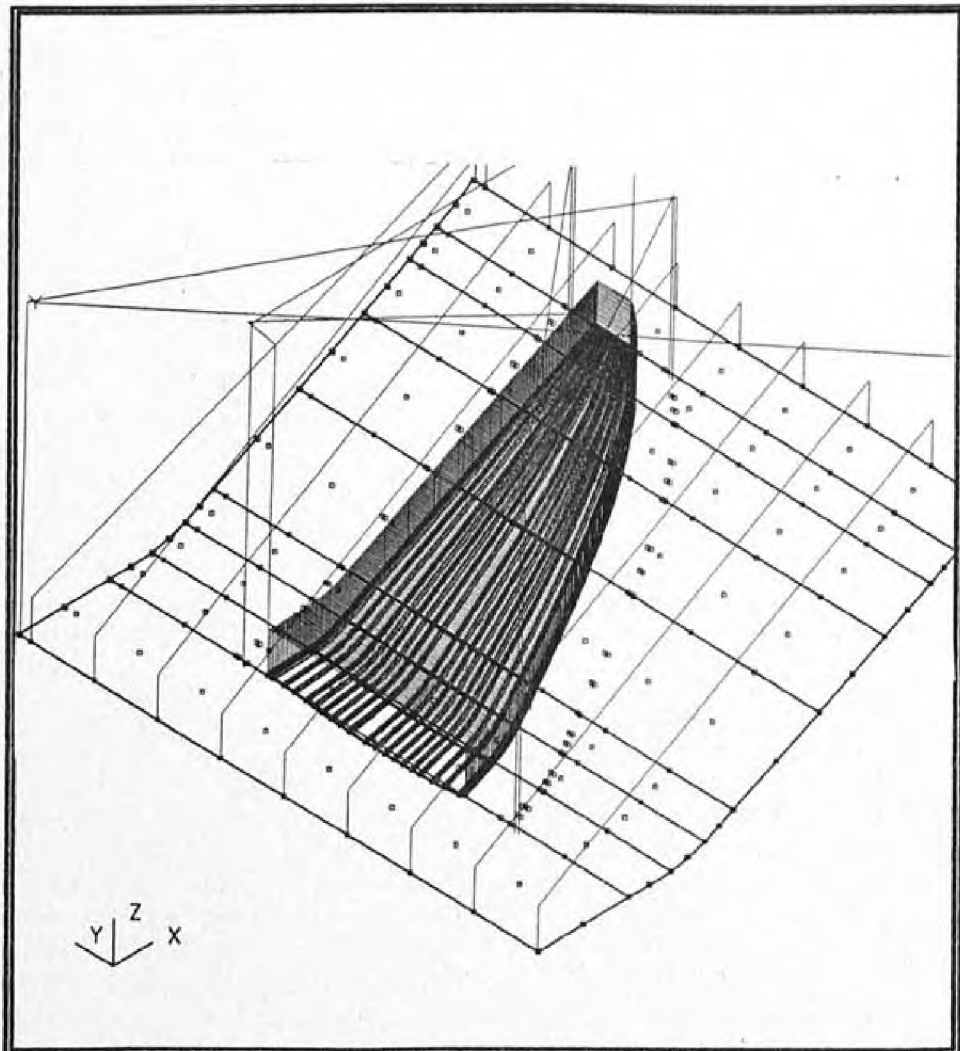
Für die Form errechneten Fräsbahnen des linken Winglets
